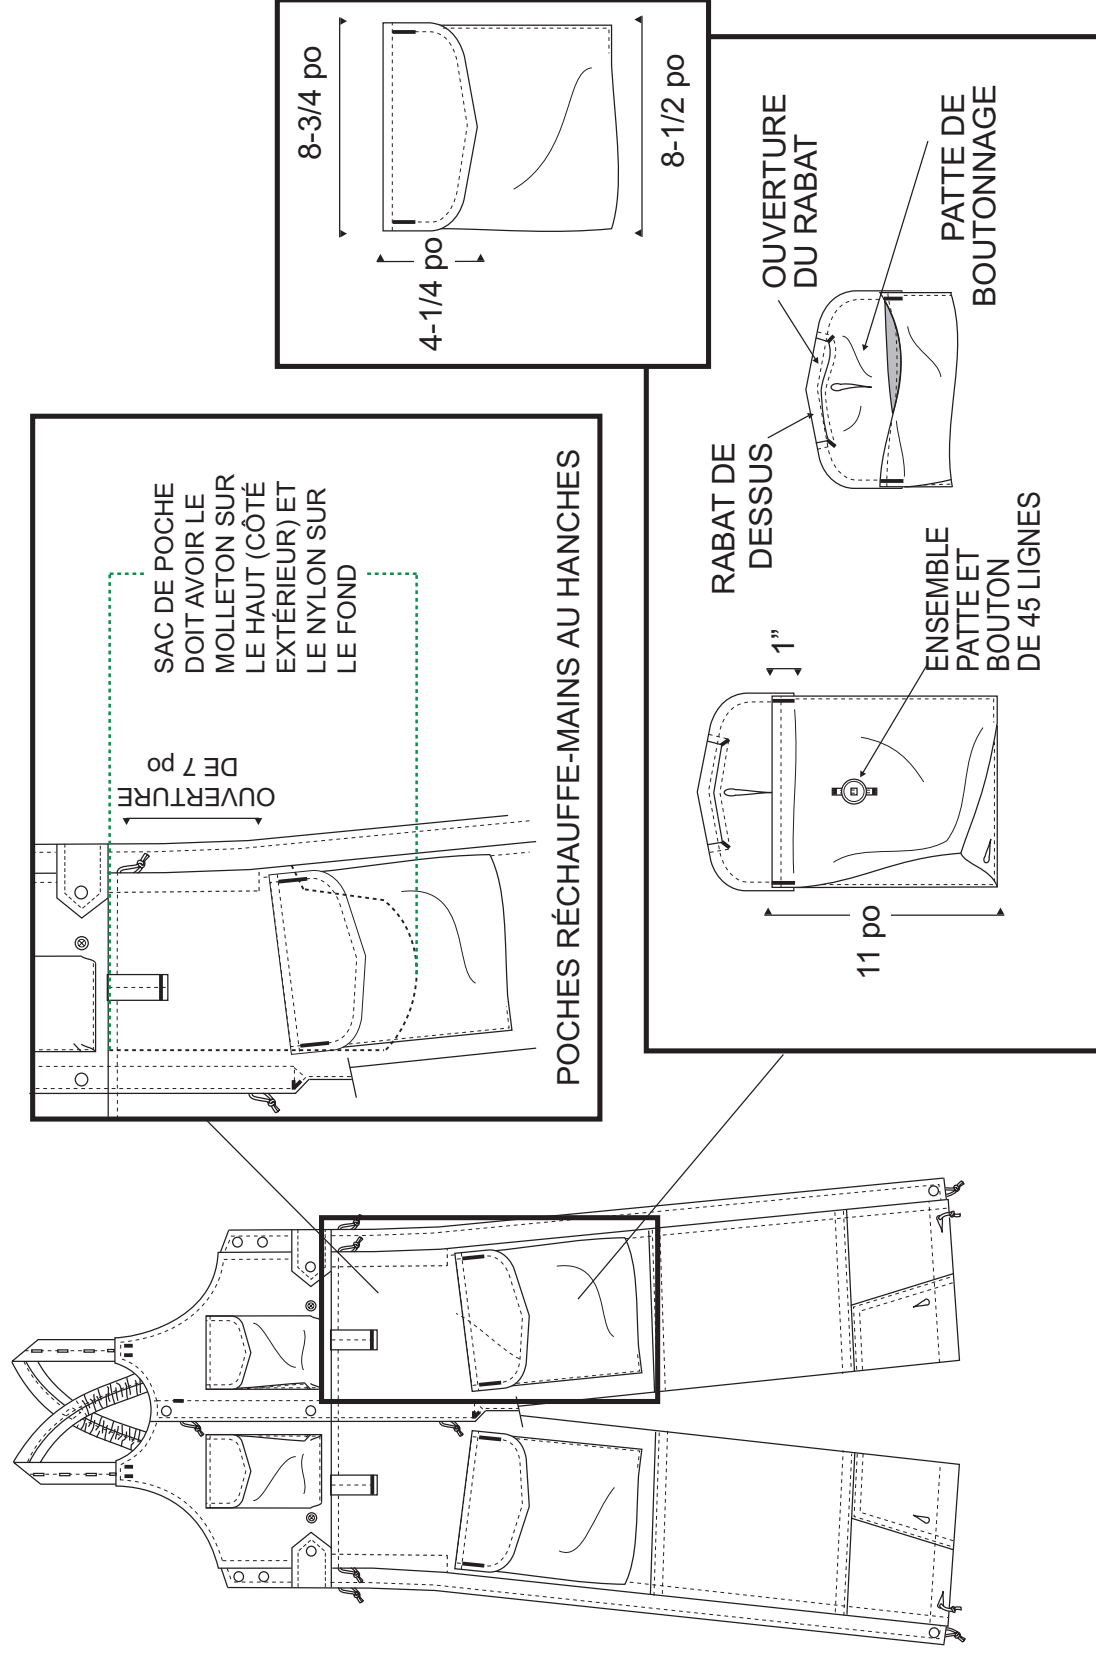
DIMENSIONS DES COMPOSANTS DU VÊTEMENT
